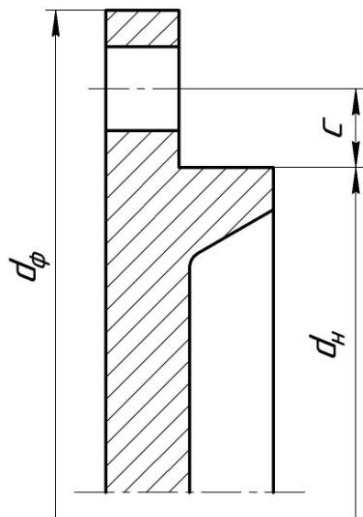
Размеры конструктивных элементов крышки подшипника
